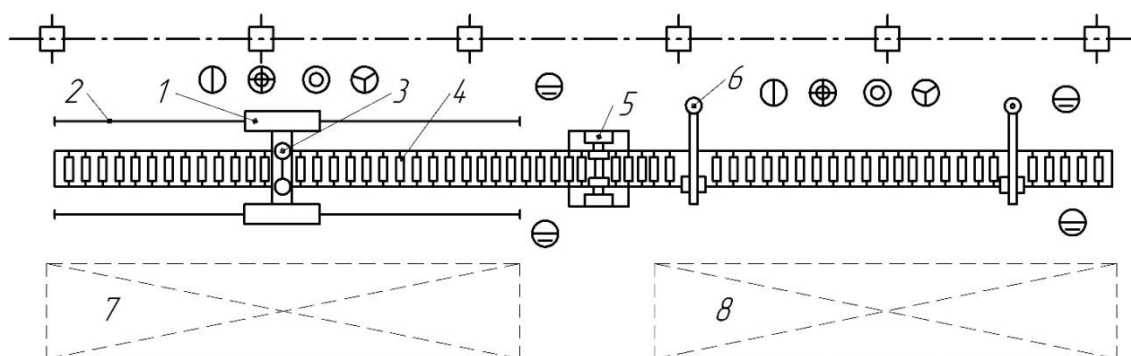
Планировка участка поточной линии сборки, сварки и правки подкрановых балок:
